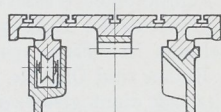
Schlittenführung an Werkzeugmaschinen.
